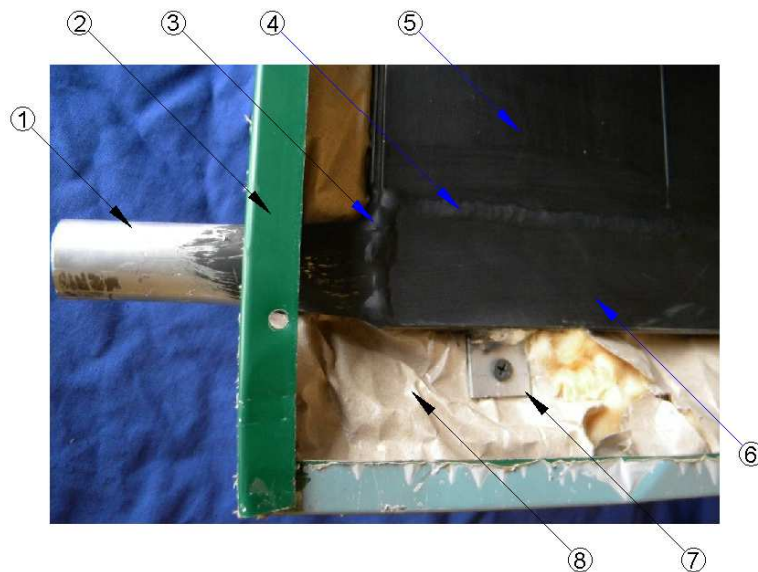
Detalle constructivo colector. 1- Tubo entrada de agua. 2- Caja de chapa. 3- Soldadura tubo entrada a perfil U. 4- Soldadura perfil U a perfil placa tubular. 5- Perfil placa tubular. 6- Perfil U. 7- Oreja para fijación de placa. 8- Aislante.
